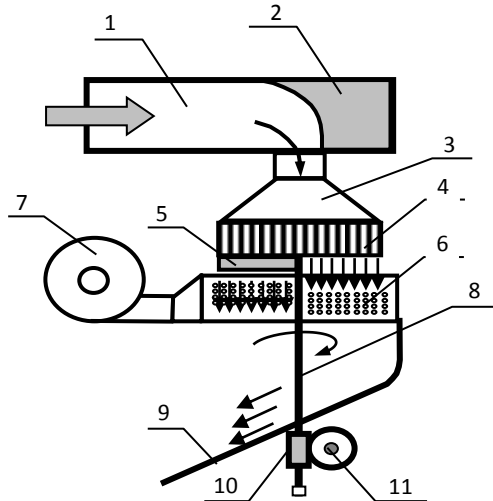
Схема механізму різання коротких макаронних виробів по дисковій матриці: 1 - пресувальний пристрій; 2 - пробка; 3 - пресова камера; 4 - матриця; 5 - ніж; 6 - обдувочне пристрій; 7 - вентилятор; 8 - вертикальний вал; 9 - лоток; 10 - гвинтова шестірня; 11 - гвинтове колесо
